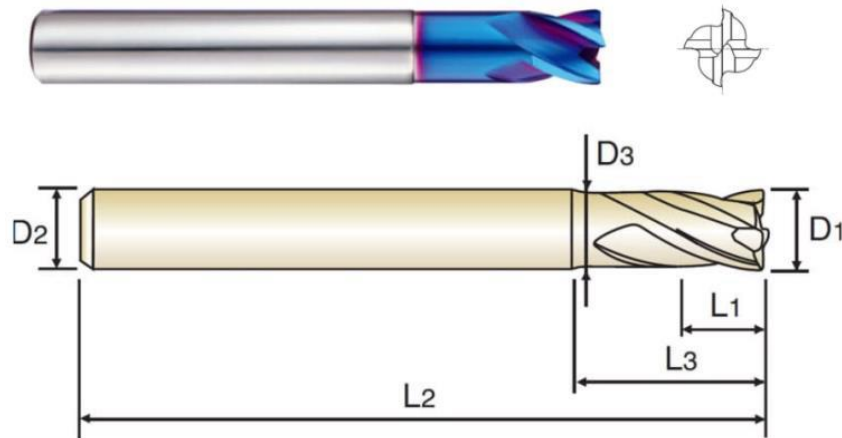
Технический чертеж концевой фрезы G8A02080 X5070.
